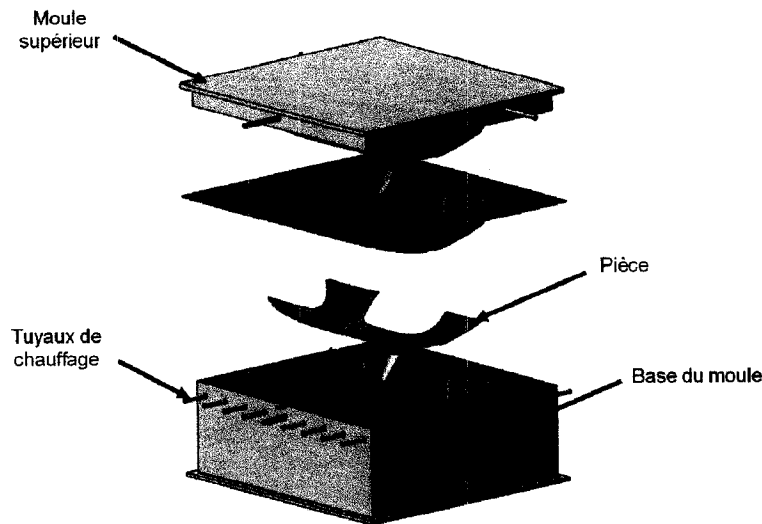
Vue détaillée du moule prototype d'après le dessin original de Louis Laberge-Lebel (2005)
